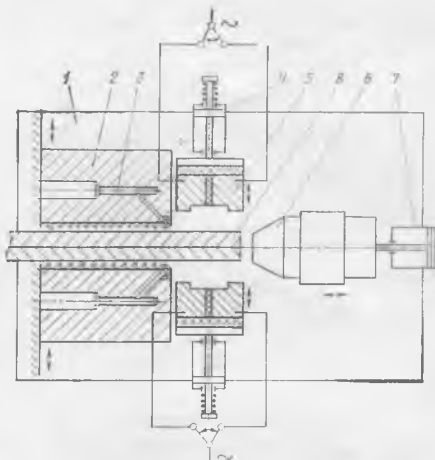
Схема рабочего органа станка для высадки головок конструкции НИИЖБ
